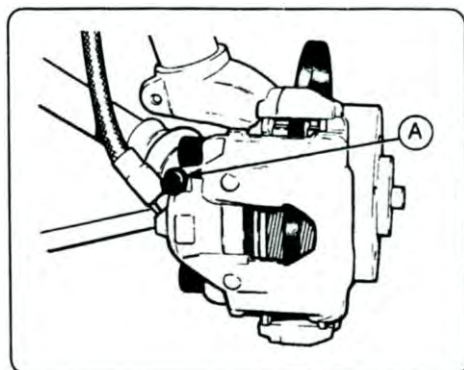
Штуцер для удаления воздуха «А» из дискового тормоза расположен на суппорте
